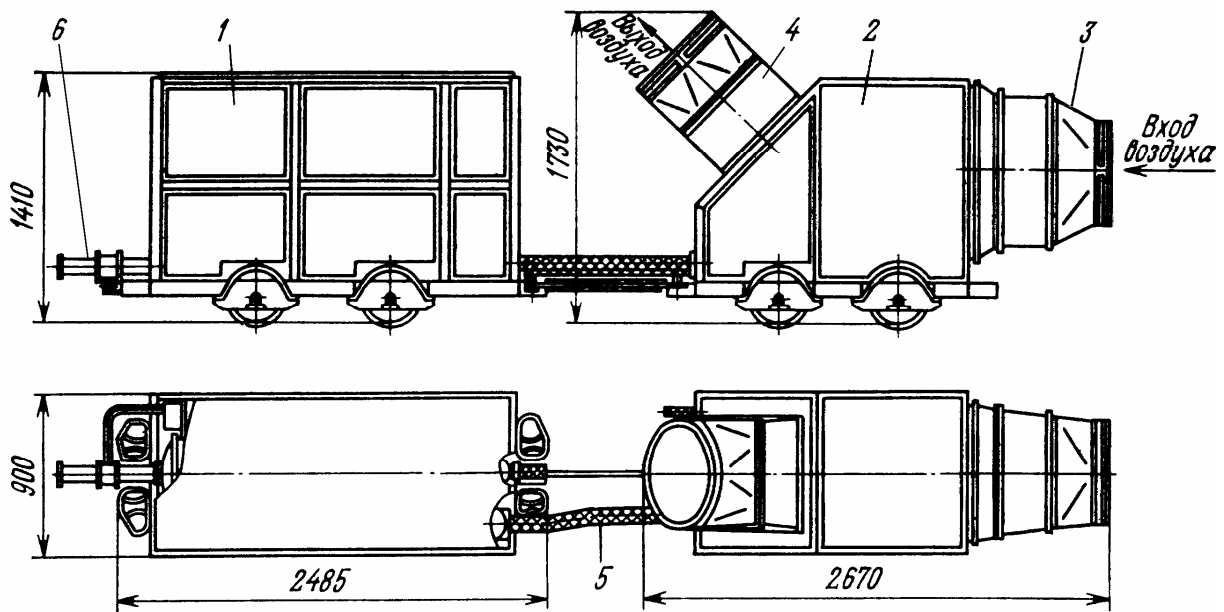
Кондиціонер КПШ-90: 1 – компресорно-конденсаторний агрегат; 2 – повітрообробний агрегат; 3 – патрубок входу охолодженого повітря; 4 – патрубок виходу охолодженого повітря; 5 – гнучкі рукави для рідкого і газоподібного холодоагенту; 6 – патрубки підведення води
